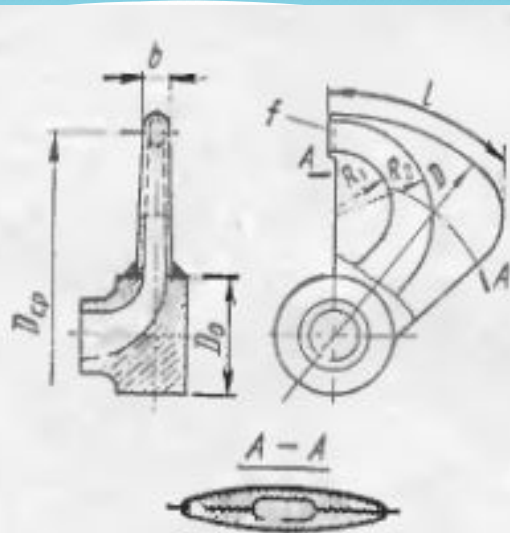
Черпаки профилеобразного типа № 1; 2; 6; 9
